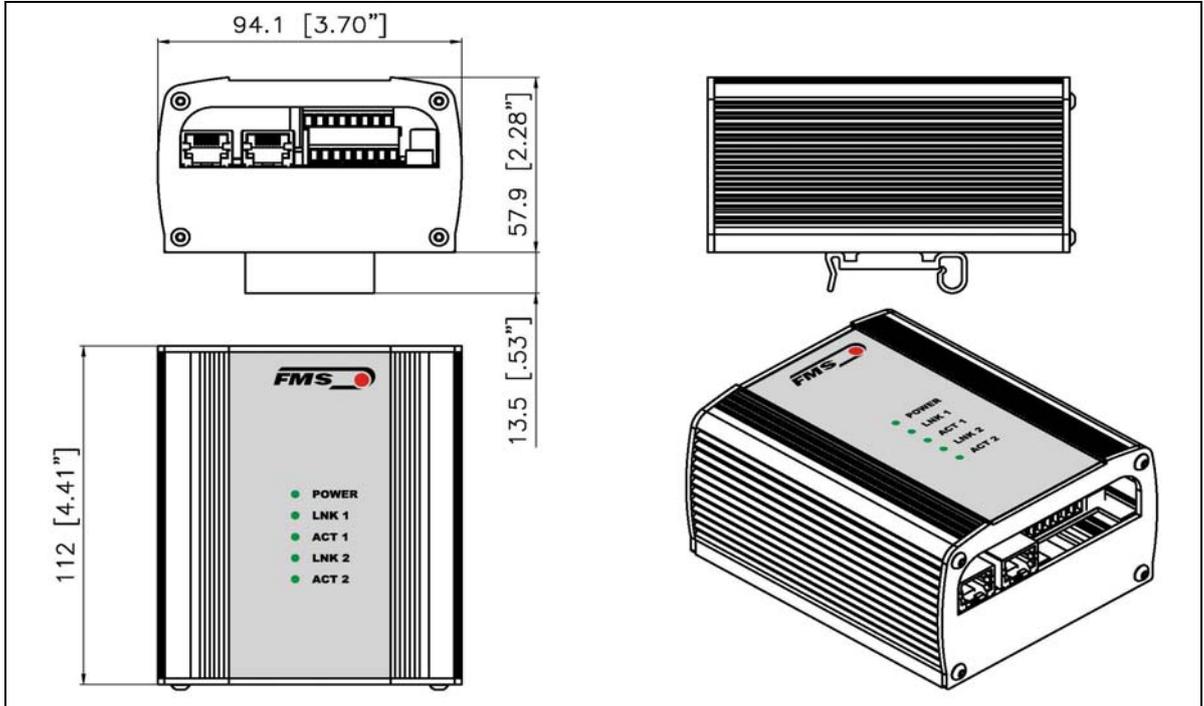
EMGZ 490.R Gehäuse für DIN-Schienenmontage
